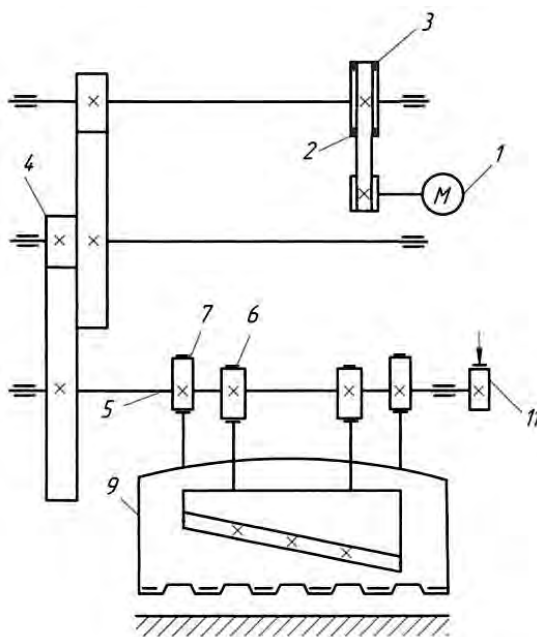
Схема кривошипного гибочно-штамповочного горизонтального пресса (бульдозера)
